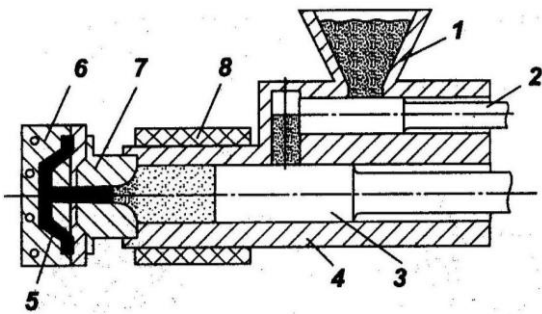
Схема лиття пластмас під тиском: 1 – бункер; 2 – дозатор; 3 – поршень; 4 – циліндр; 5 – заготовка; 6 – форма; 7 – сопло; 8 – електронагрівач
